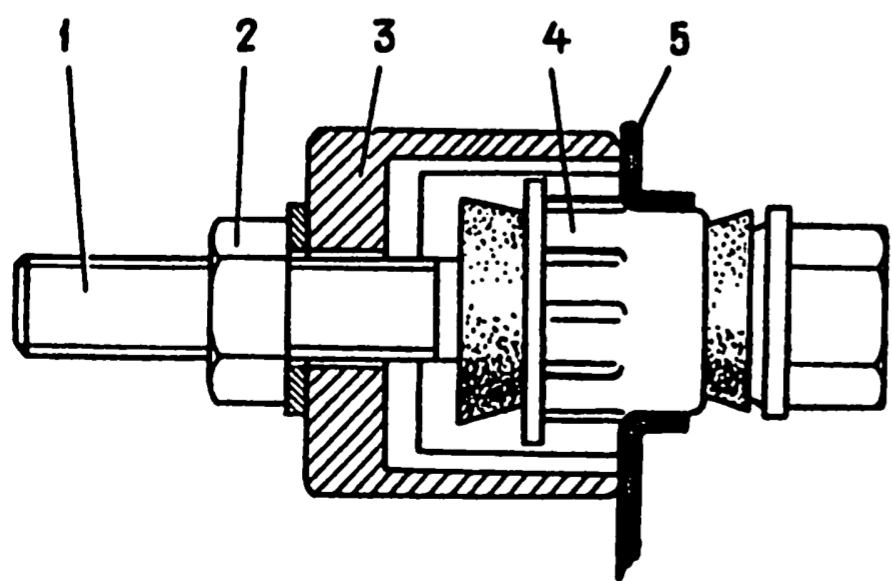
Схема выпрессовки шарнира верхнего рычага: 1 - болт; 2 - гайка; 3 - стакан приспособления А.47046; 4 - шарнир; 5 - верхний рычаг
